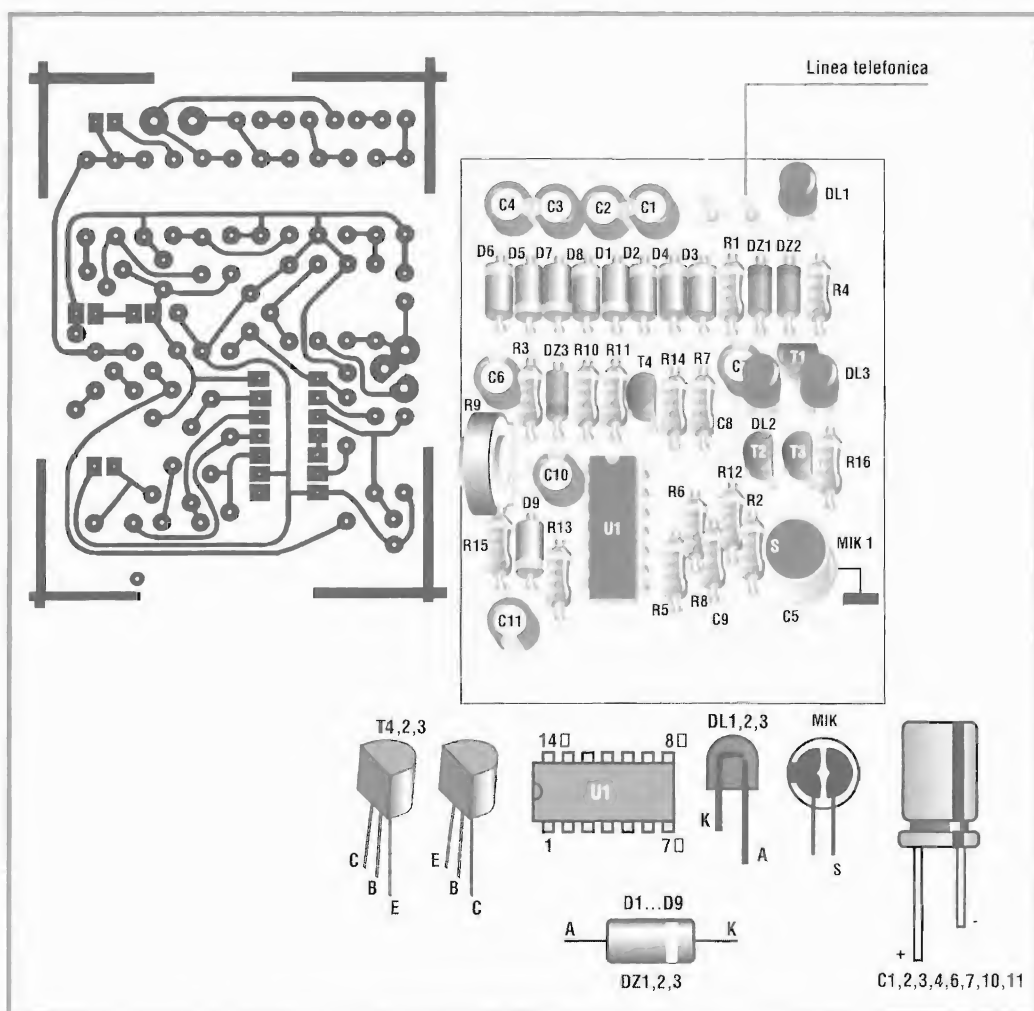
3.23. Circuito stampato e montaggio dei componenti della sentinella.
